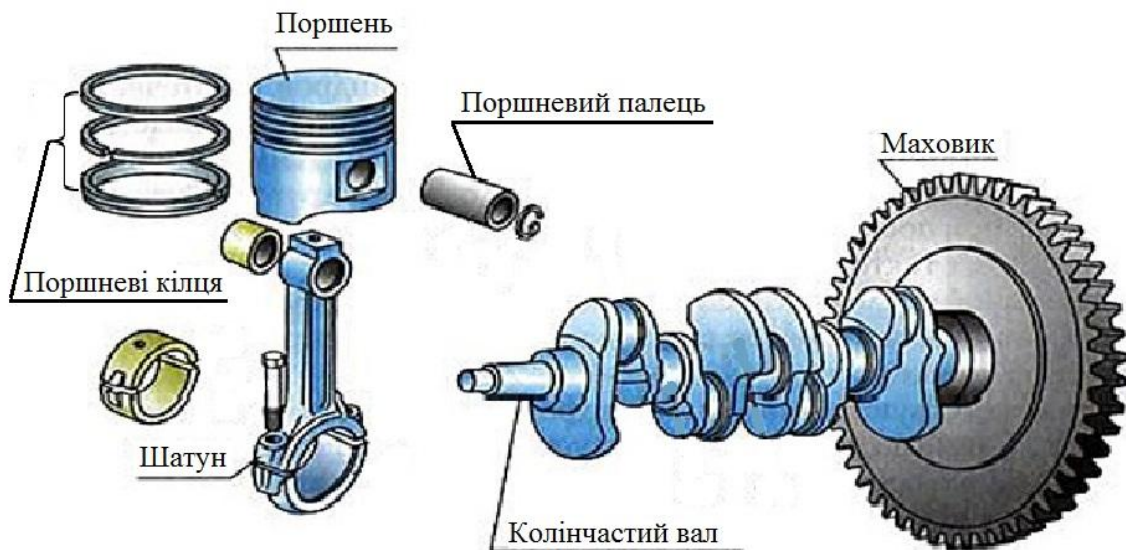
Рухомі деталі кривошипно-шатунного механізму
